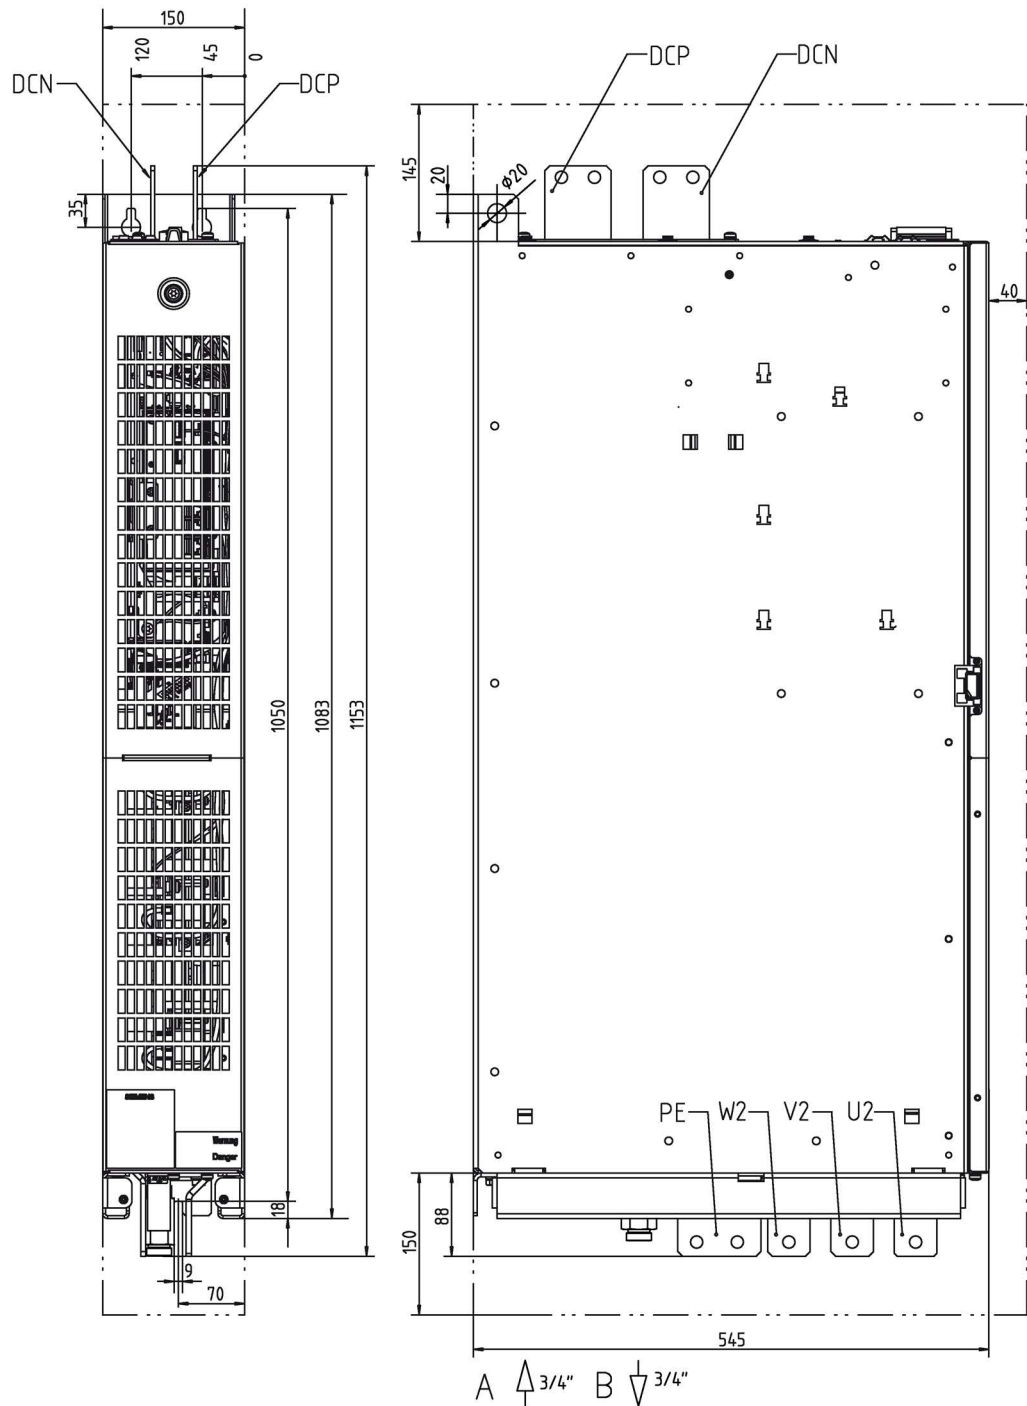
Габаритный чертёж модуля двигателя, типоразмер GXL. Вид спереди, вид сбоку
